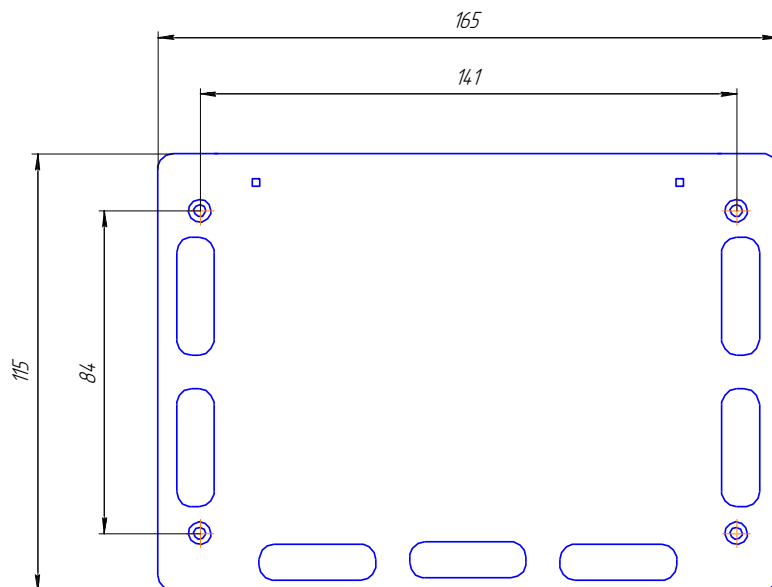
Разметка крепления АМЗ в пластмассовом корпусе.
